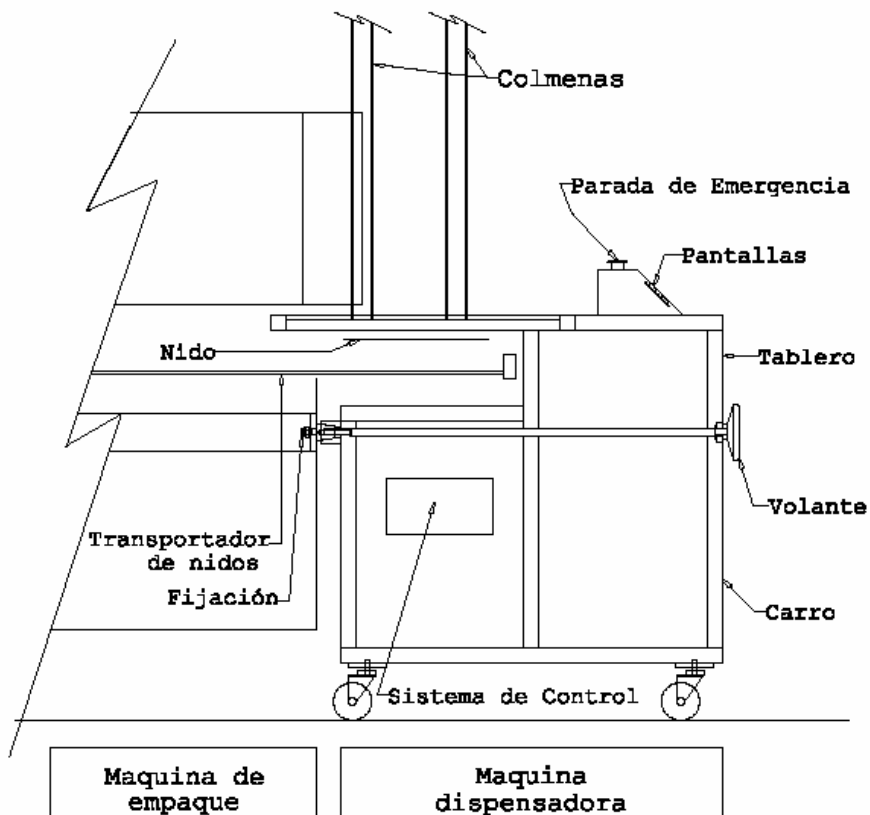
Vista lateral de la máquina dispensadora presentada en la máquina de empaque.
